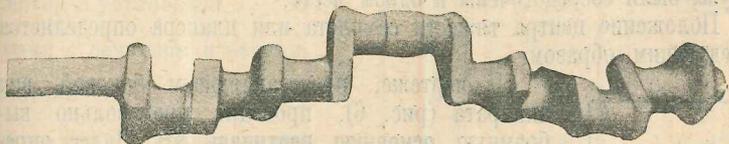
Поковка коленчатого вала для 12-цилиндрового авиадвигателя, изготовленная на заводе Веккерса (Англия).
